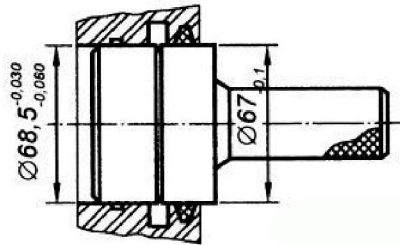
Оправка для обжатия набивки заднего уплотнения коленчатого вала.
